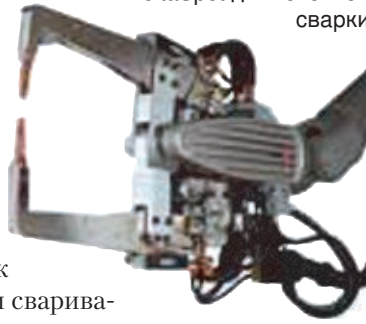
Установка DeltaSpot для точечной сварки
